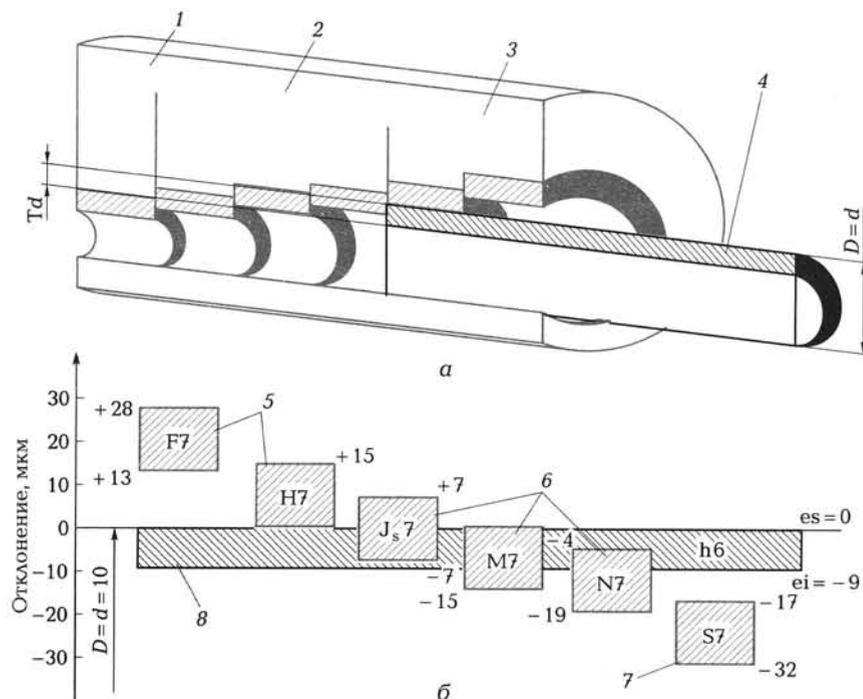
Расположение полей допусков отверстий и валов в системе вала (а) и схемы расположения полей допусков для различных посадок (б):
